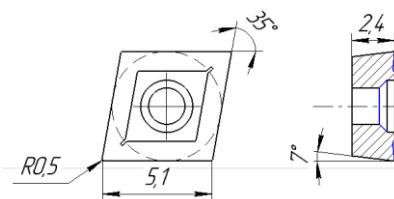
Пластина для сверления 880-0202W0,5H-P-GR
